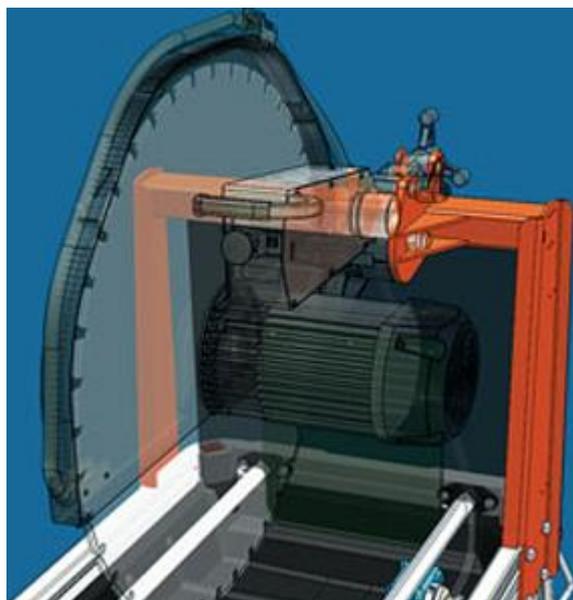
Направляющая режущей головы камнерезного станка EXPERT 700.
